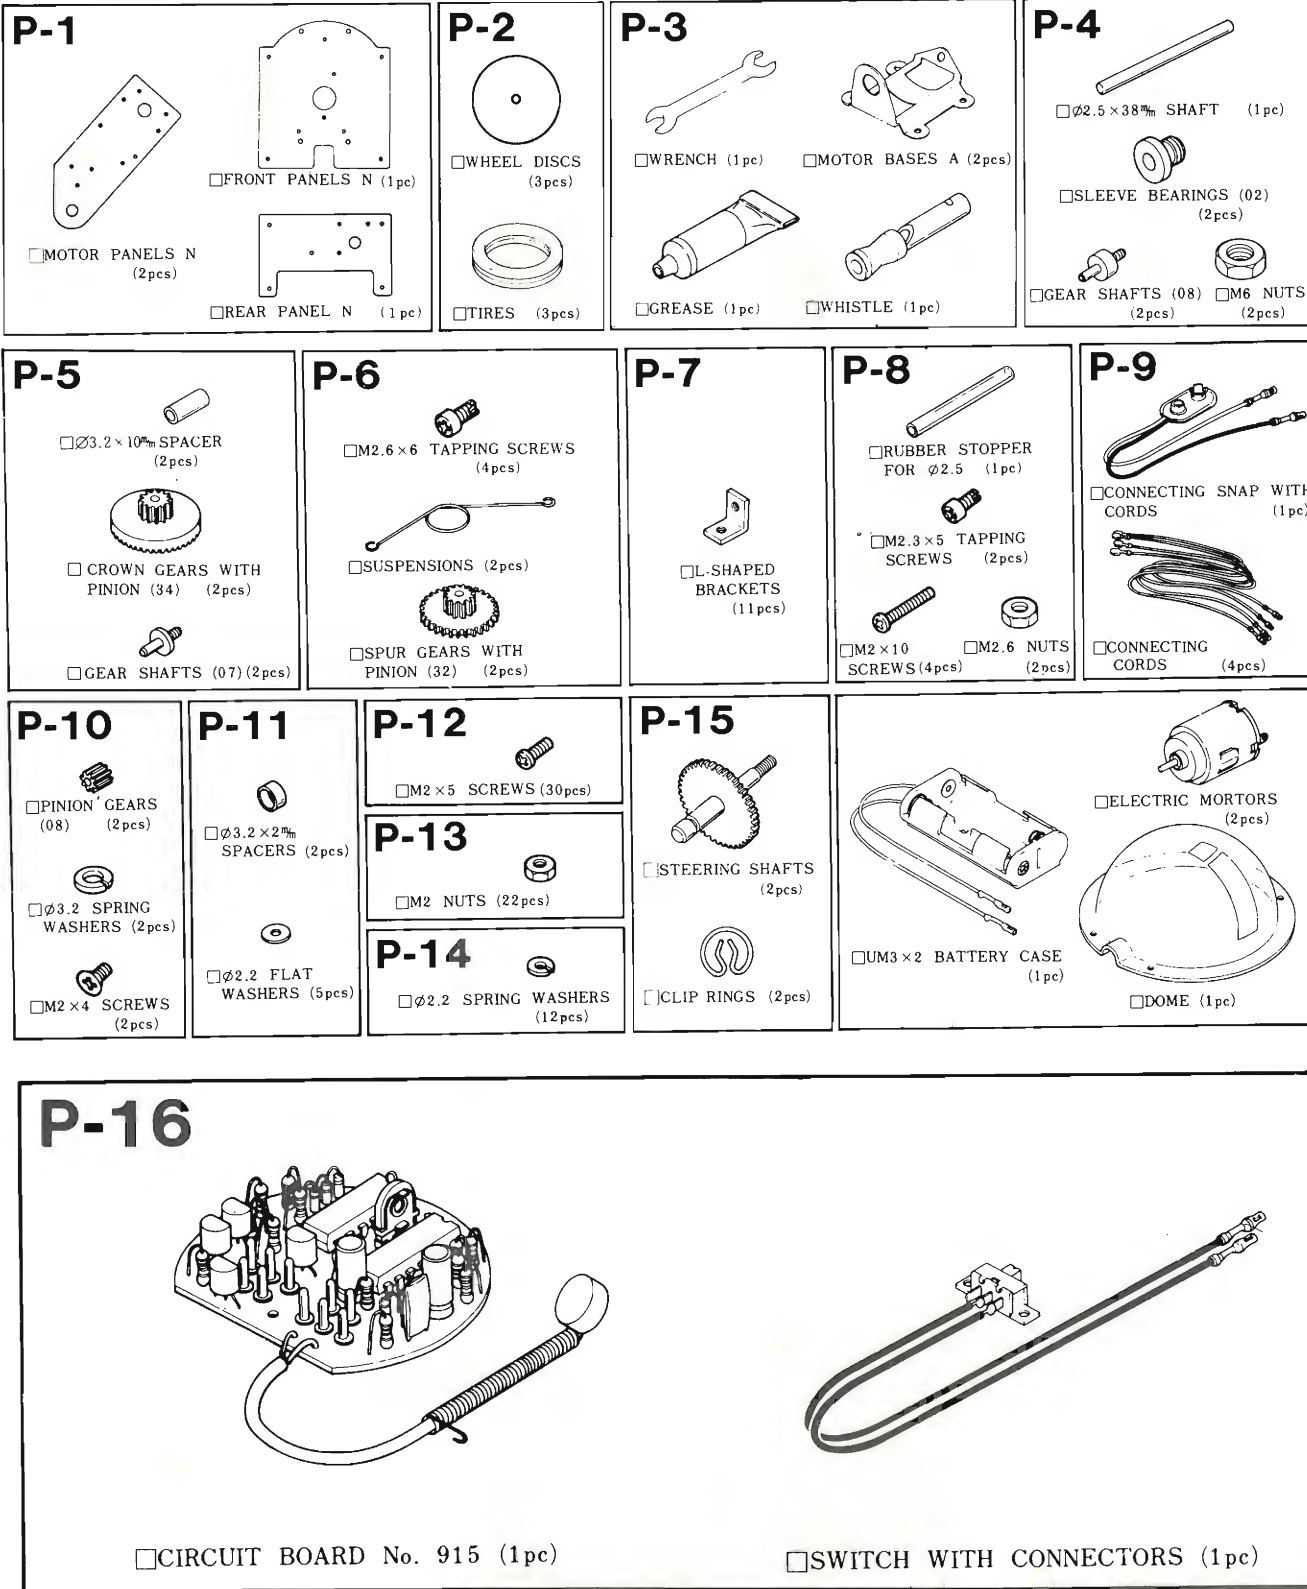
Ecco le varie parti componenti il kit del Piper Mouse.
